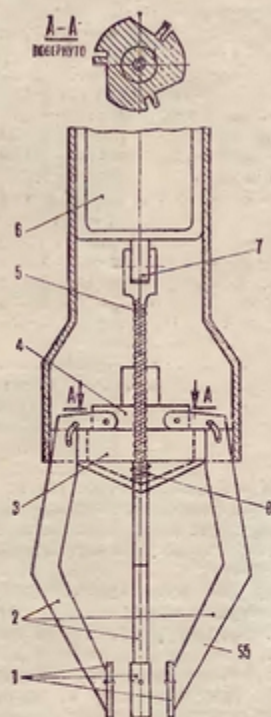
Конструкция «кисти»: 1 — платформы захватов, 2 — захваты, 3 — фланец, 4 — гайка привода, 5 — червяк, 6 — электродвигатель, 7 — вал, 8 — упорная пружина.
